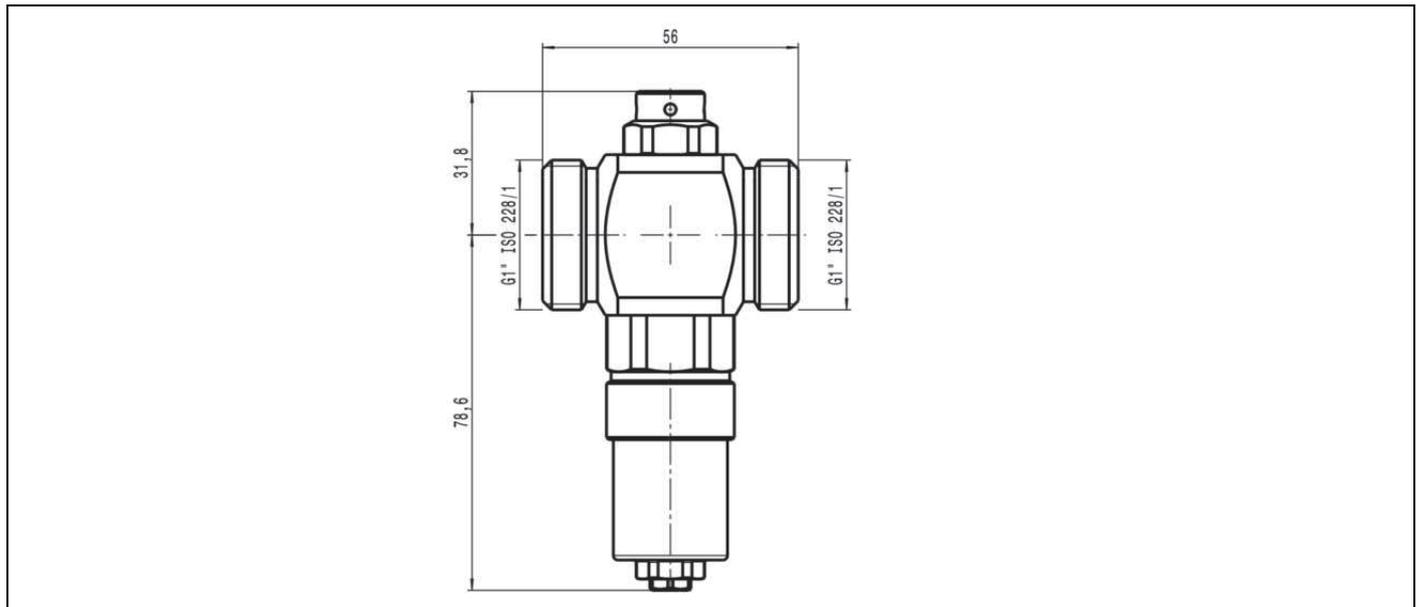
Abmessungen Thermisches Entleerungsventil
